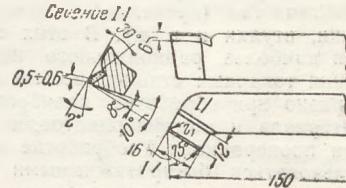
Эскиз резца для проточки грузового вала паровой лебедки
